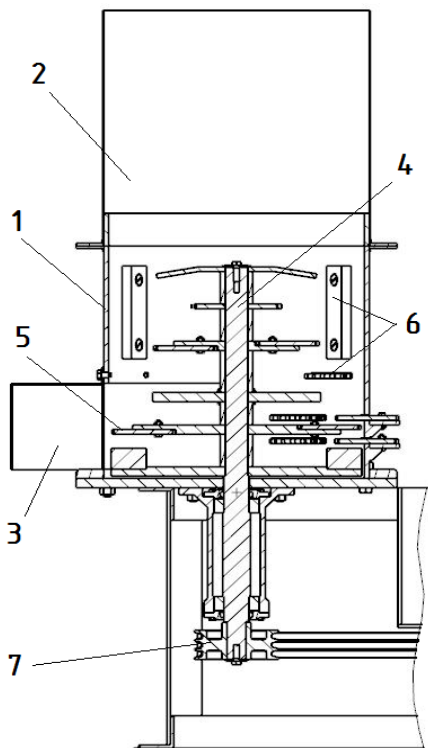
Конструктивная схема дробилки с многолезвийными рабочими органами
